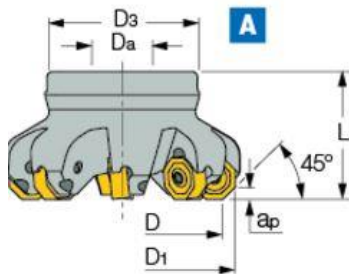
Freză frontală SOF45 8/16-D0-04-22R [5]
